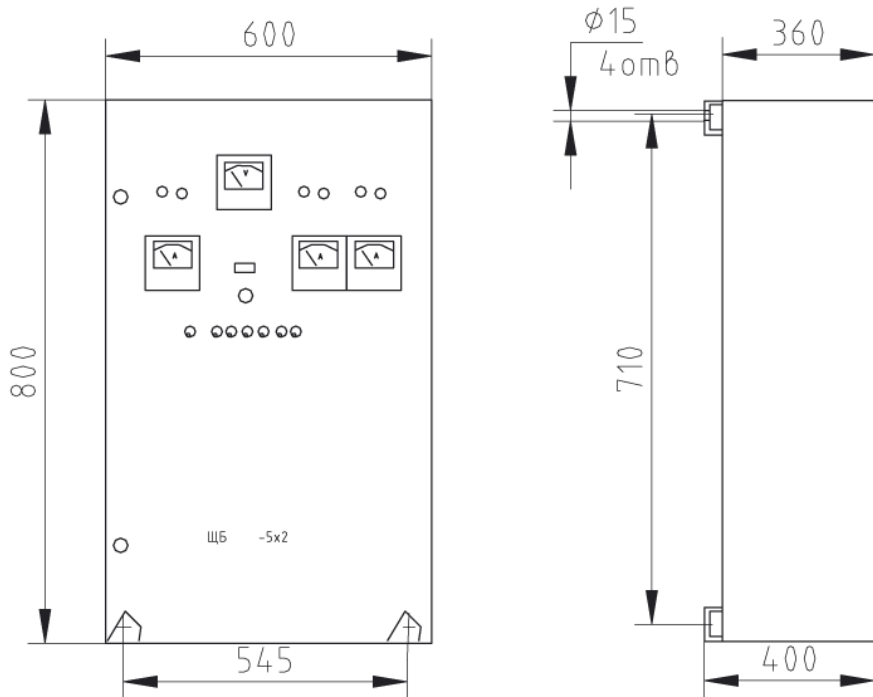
Габаритный чертёж щитов ЩБ 60/630-5х2, ЩБ 24/630-5х2
